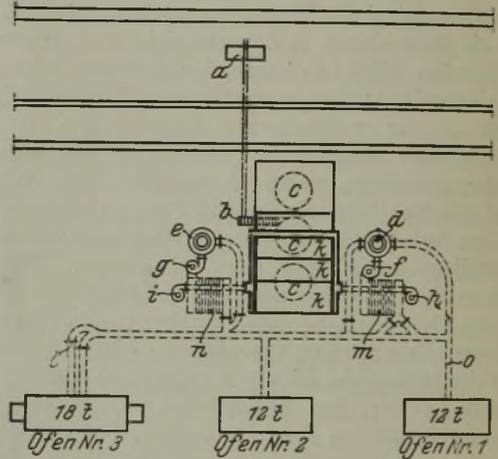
Lageplan des Siemens-Martin-Werks.
